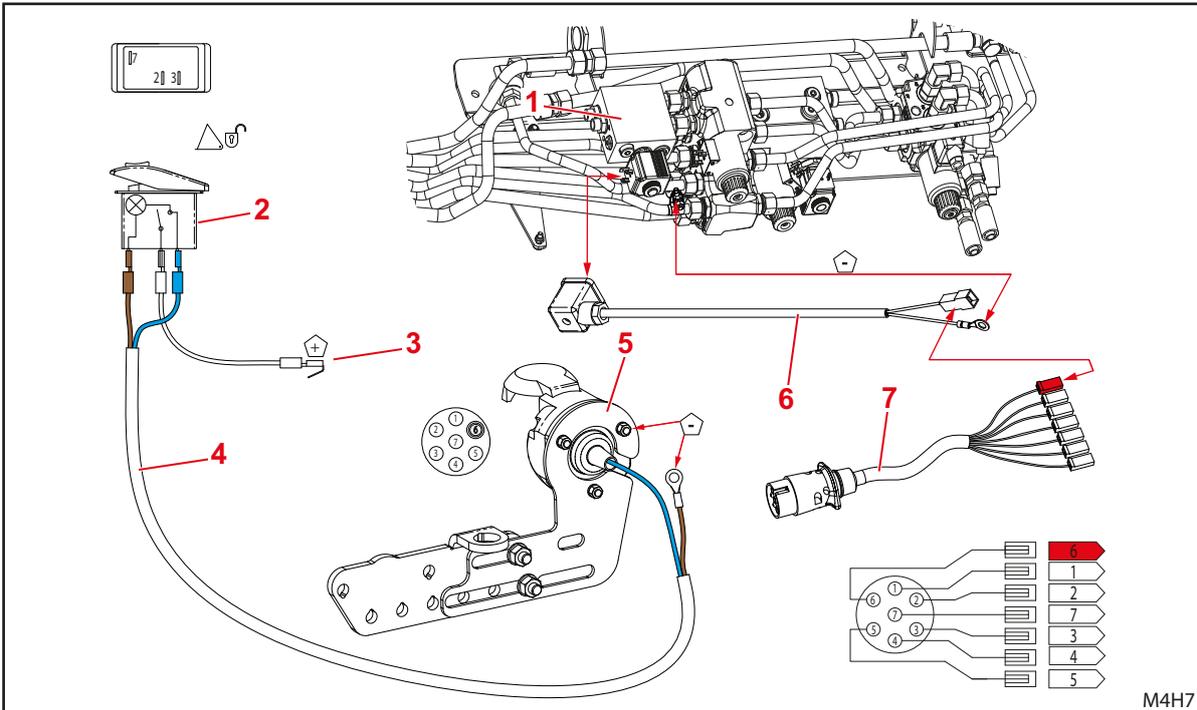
Installare il bloccaggio idraulico degli attrezzi
